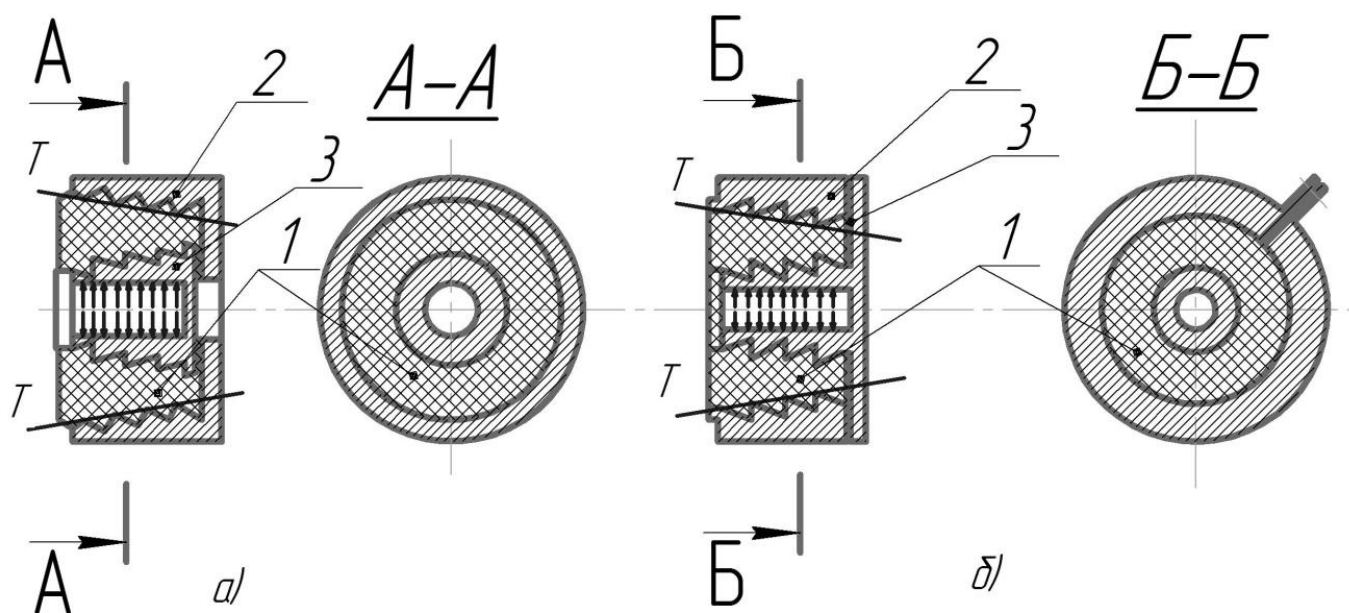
Самозаклинювальні з'єднання деталей з АКМ: а) кососиметричне; б) симетричне; 1 – армований композиційний матеріал; 2, 3 – нероз'ємні (а), роз'ємні (б) металеві обойми [14]
